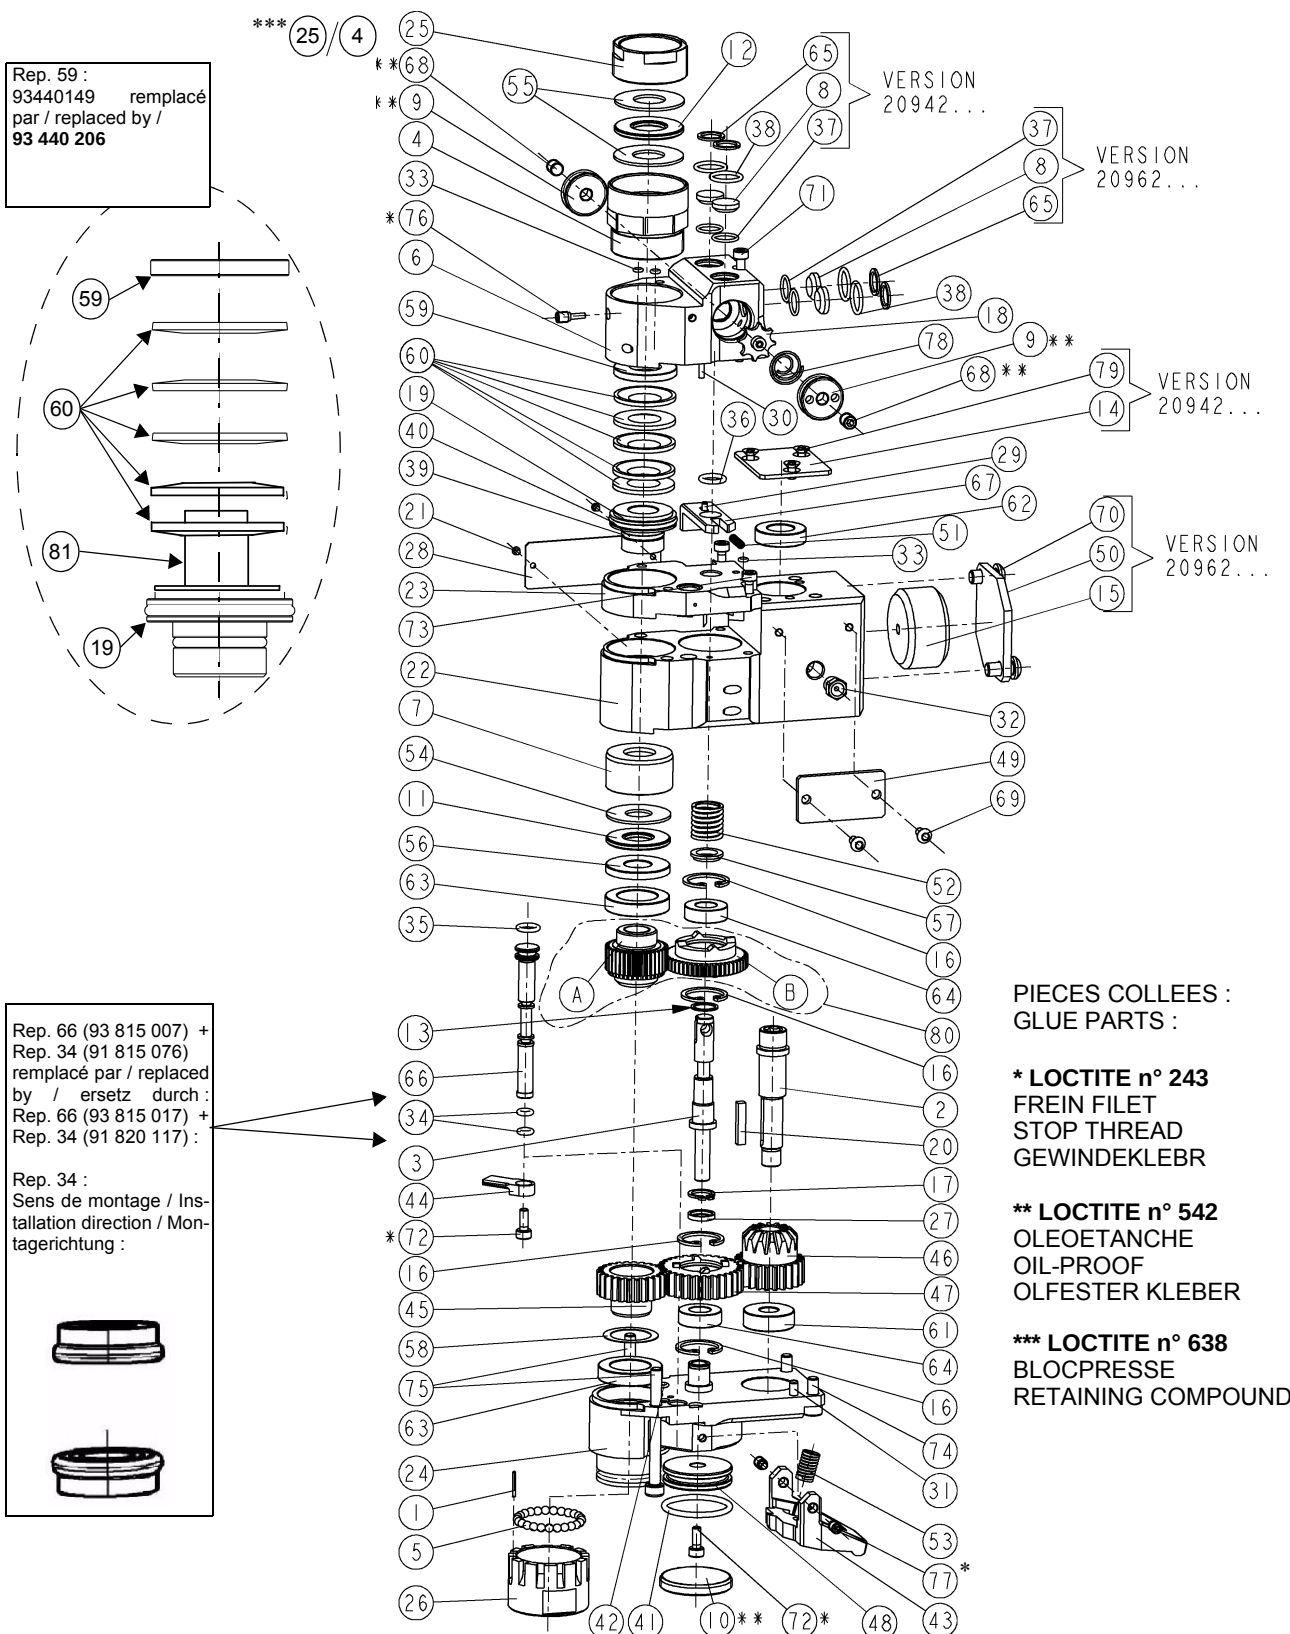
Sauf vitesse 6000 trs/mn · Except speed 6000 rpm · Ausser Drehzahl 6000 UpM
